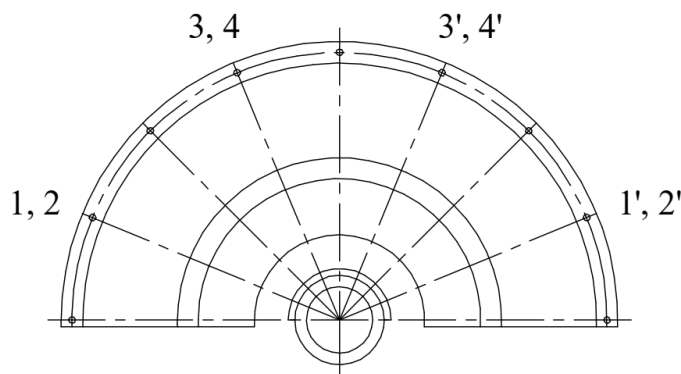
Розташування точок вимірювання у поздовжніх перерізах на корпусі статора турбогенератора (вид зі сторони контактних кілець)
